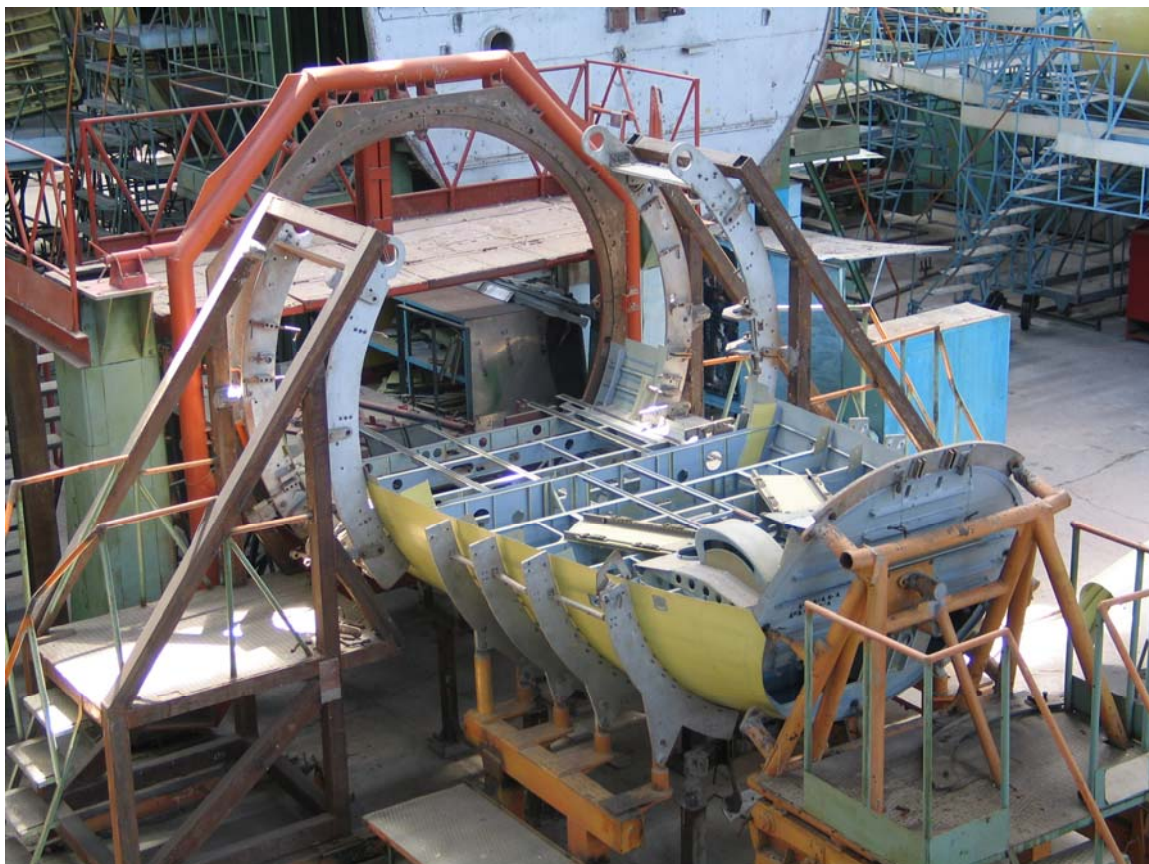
Приспособление для сборки нижней частей Ф-1
